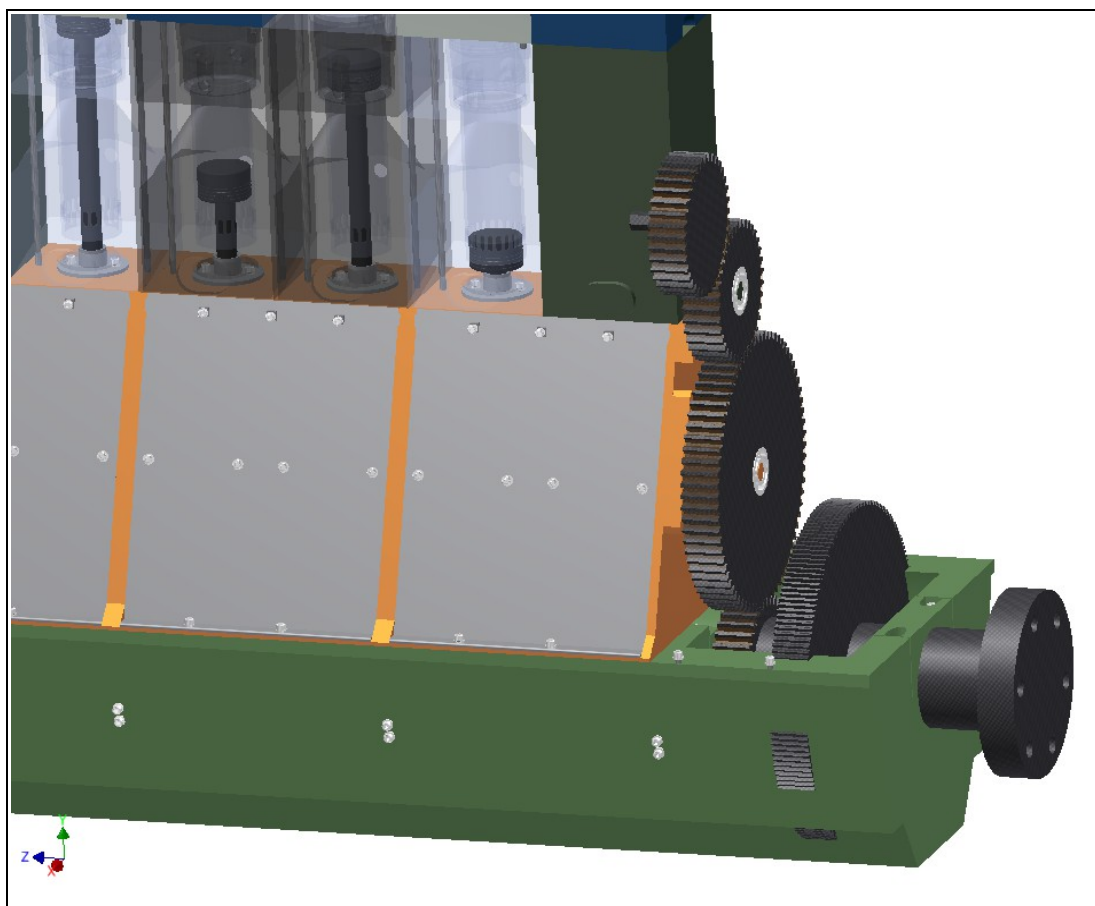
Tren de engranajes con motor, ensamble
